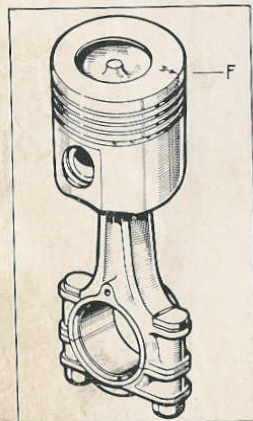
RIFERIMENTO MONTAGGIO PISTONE.
